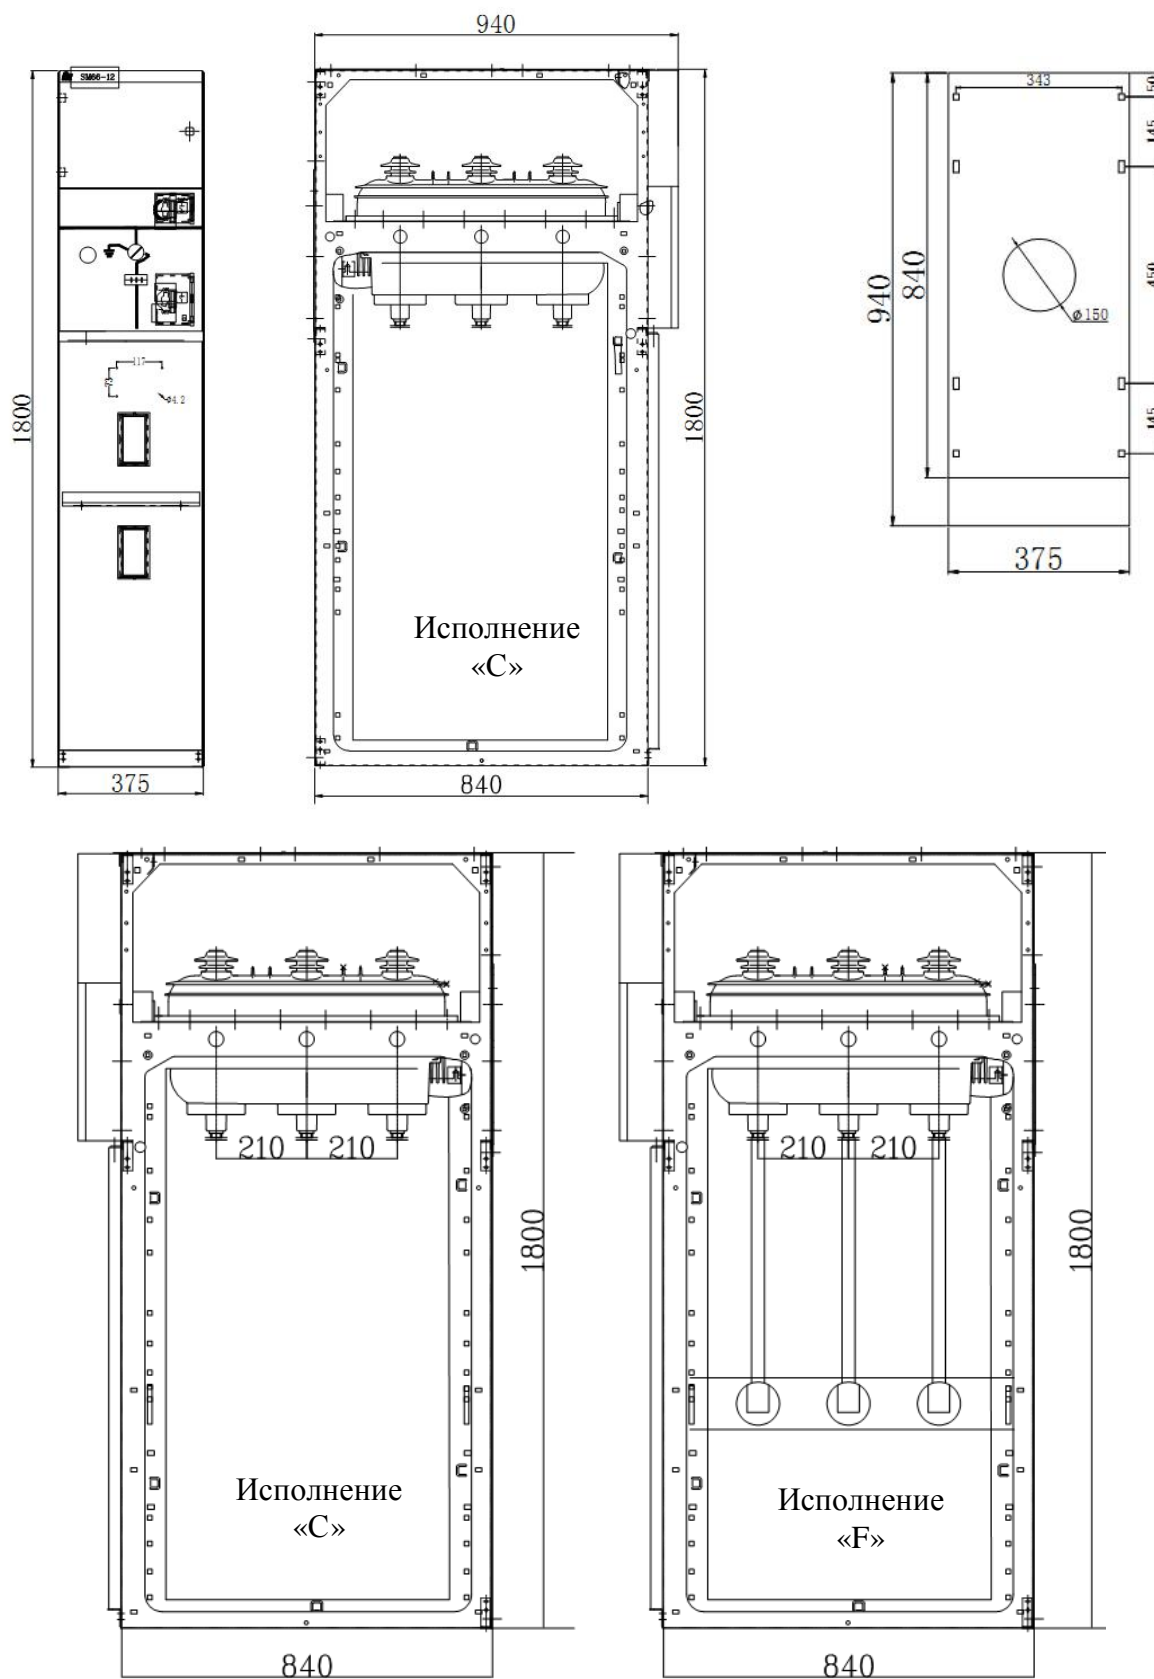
Габаритные и установочные размеры КРУЭ-БЭМН исполнений «С» и «F»
